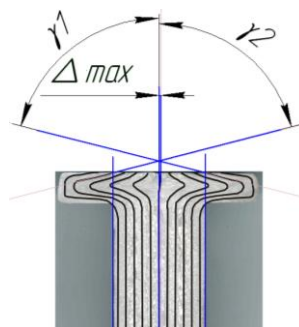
волокниста будова заготовки типу стрижня з фланцем
